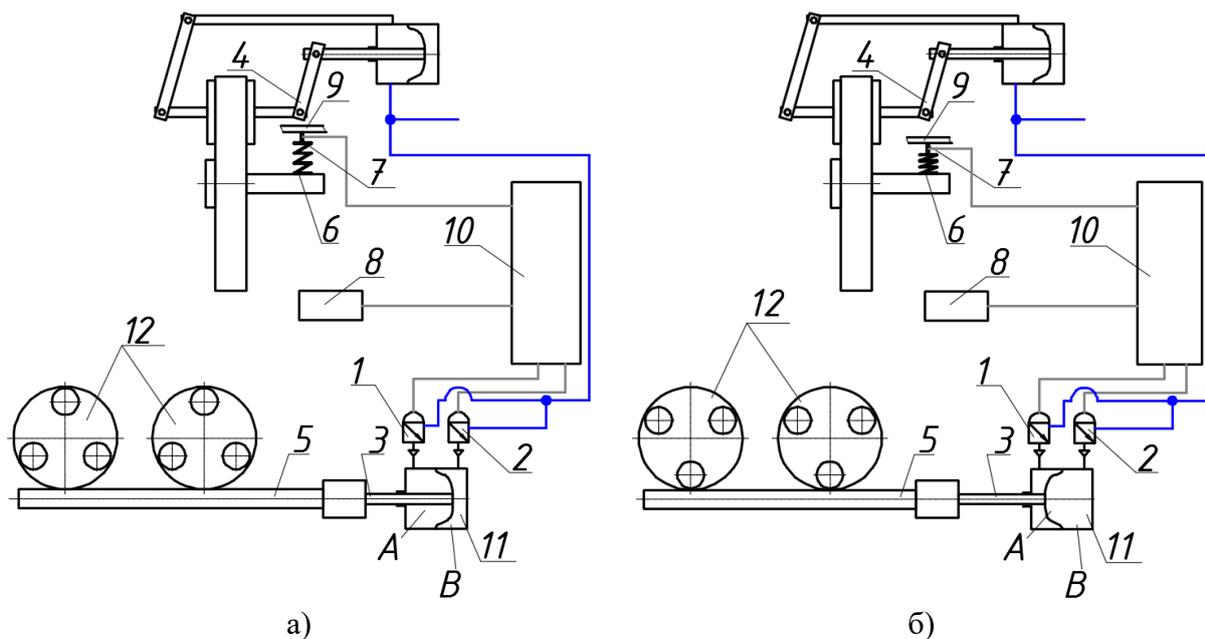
Схема работы привода регулирующего механизма тормозного устройства дисково-колодочного типа
